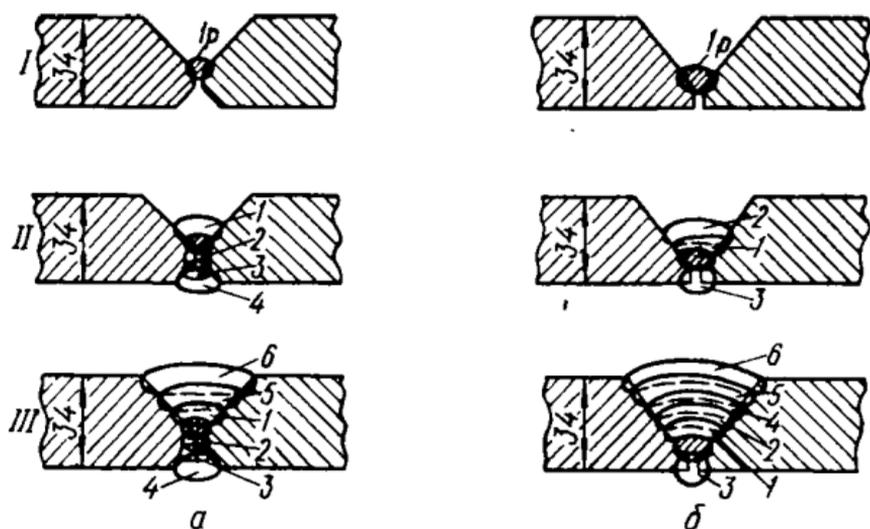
Схема наложения слоев при автоматической сварке под флюсом сферической оболочки толщиной 34 мм:
